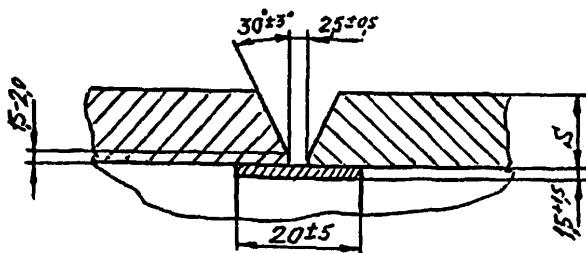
Подготовка кромок стыковых соединений на подкладном кольце
